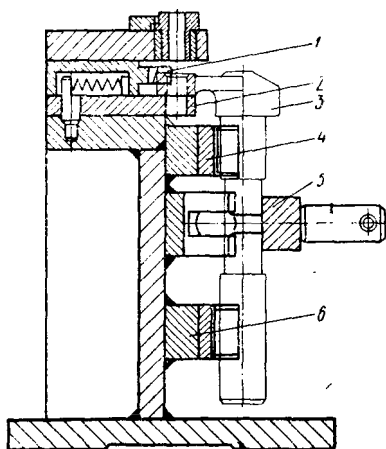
Приспособление для обработки отверстий в деталях технологического ряда ВР-01
